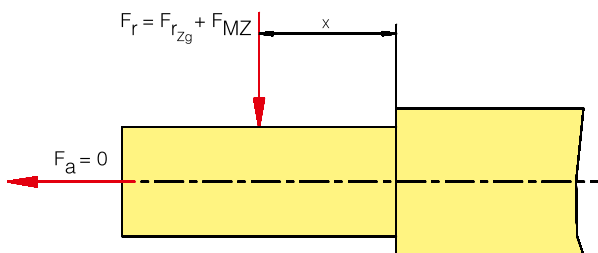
Kraftantrieb bei horizontaler Welle (Geradzahnstirnräder)
